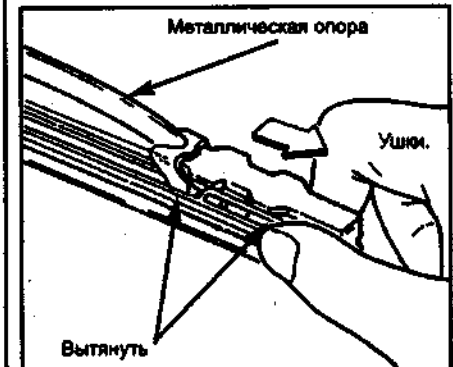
Направление снятия резиновой щетки с металлической опоры
